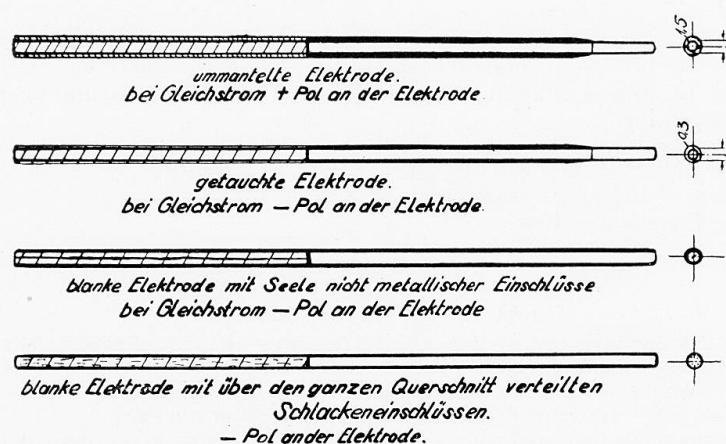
Electrodes pour soudure d'assemblage
